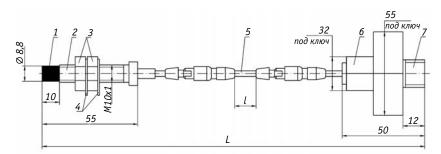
Преобразователь вихретоковый ИЦФР.408113.023: 1 – наконечник; 2 – трубка; 3 – гайка; 4 – шайба контровочная; 5 – жгут; 6 – переходник; 7 – вилка 2РМГ14Б4Ш1Е1Б
